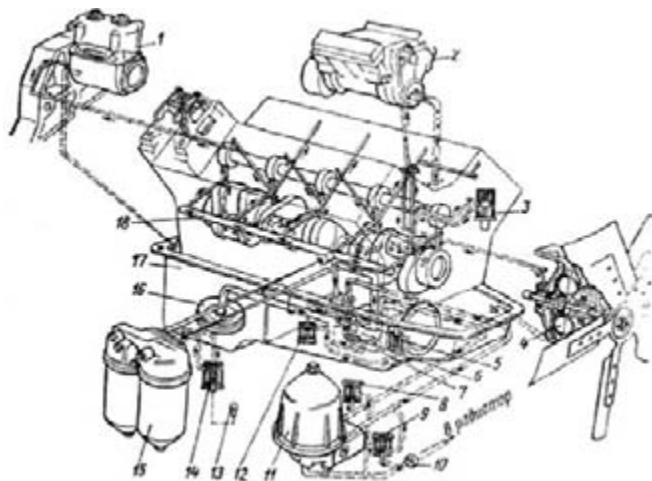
Схема смазочной системы автомобиля КАМАЗ: 1 — компрессор; 2 — топливный насос высокого давления; 3 — выключатель гидромфты; 4 — гидромфта; 5 — предохранительный клапан; 6 — клапан системы смазки; 7 — масляный насос; 8 — перепускной клапан центробежного фильтра; 9 — сливной клапан центробежного фильтра; 10 — кран включения масляного радиатора; 11 — центробежный фильтр; 12 — предохранительный клапан; 13 — сигнальная лампа засоренности фильтра очистки масла; 14 — перепускной клапан фильтра очистки масла; 15 — фильтр очистки масла; 16 — маслоприемник; 17 — картер; 18 — главная магистраль.
